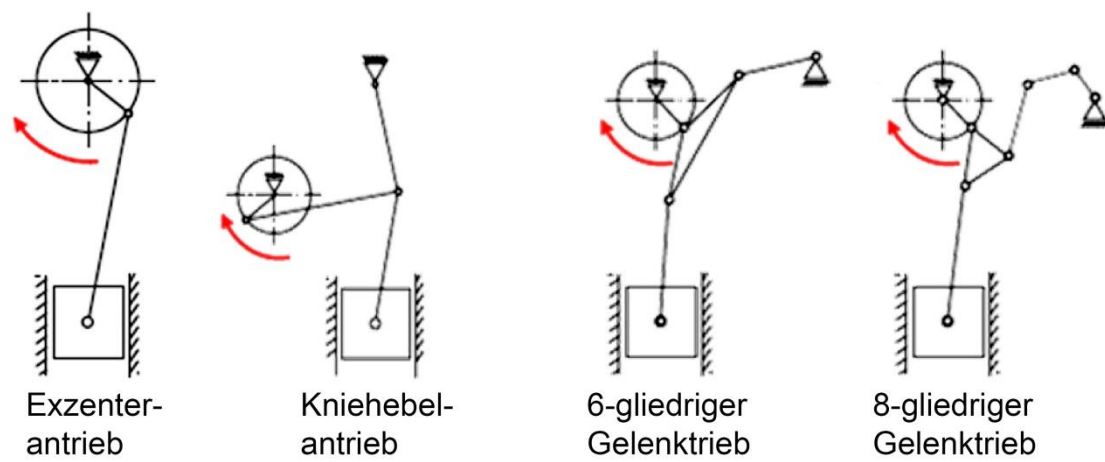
Getriebetypen für mechanische Pressenantriebe [BOGO12]
